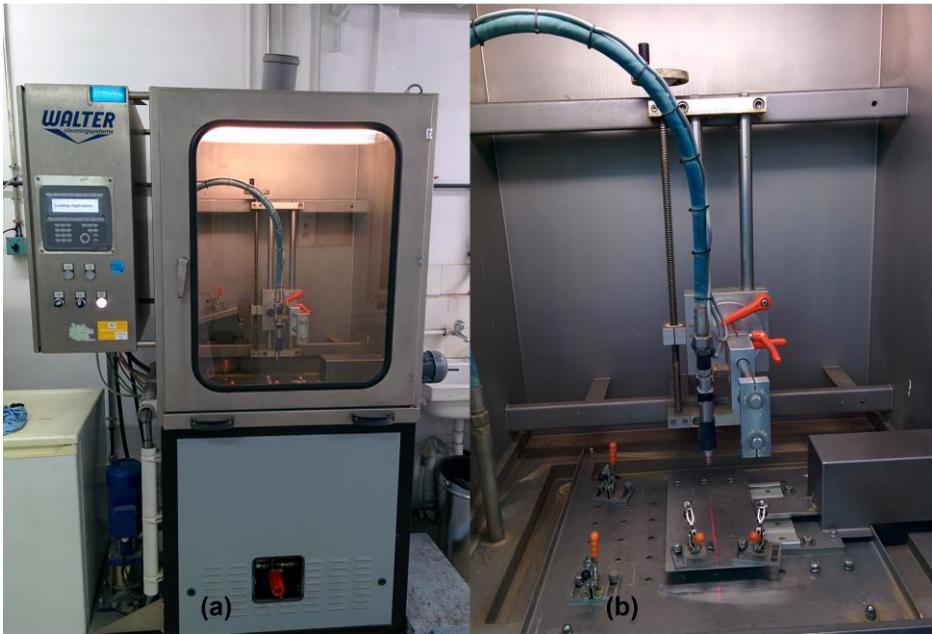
Sistema Walter de lavado a alta presión: (a) vista general, (b) vista interior.
